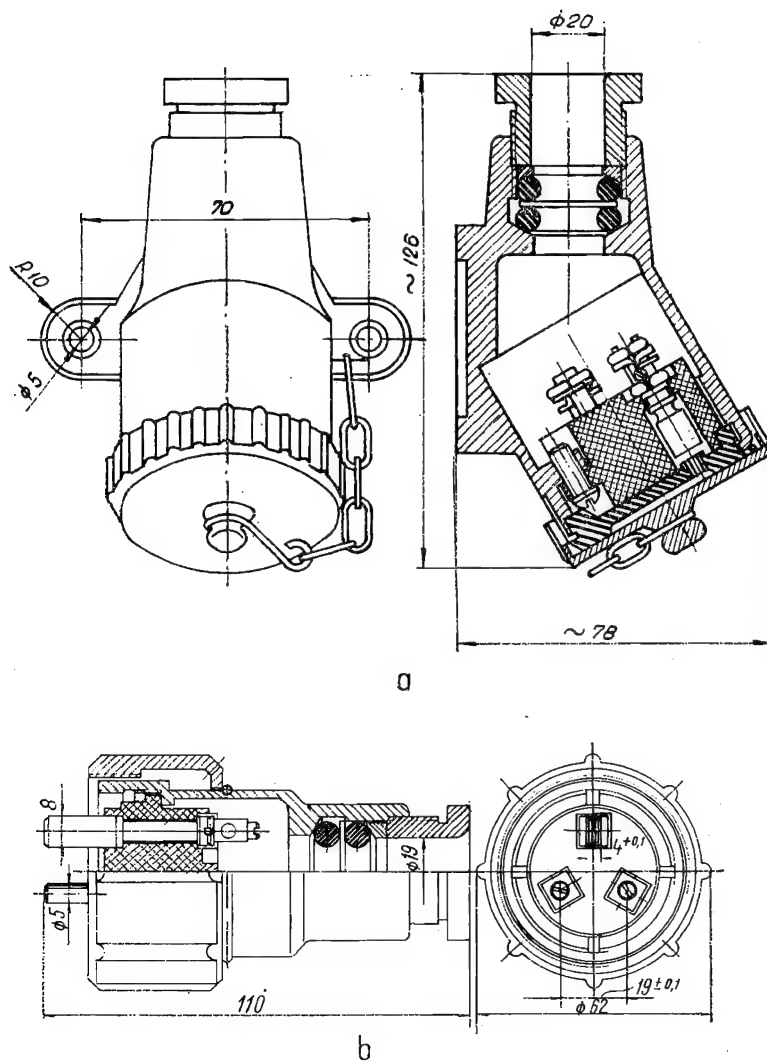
Priză și fișă tripolară de 25 A și 36 V în carcasă de silumin:
